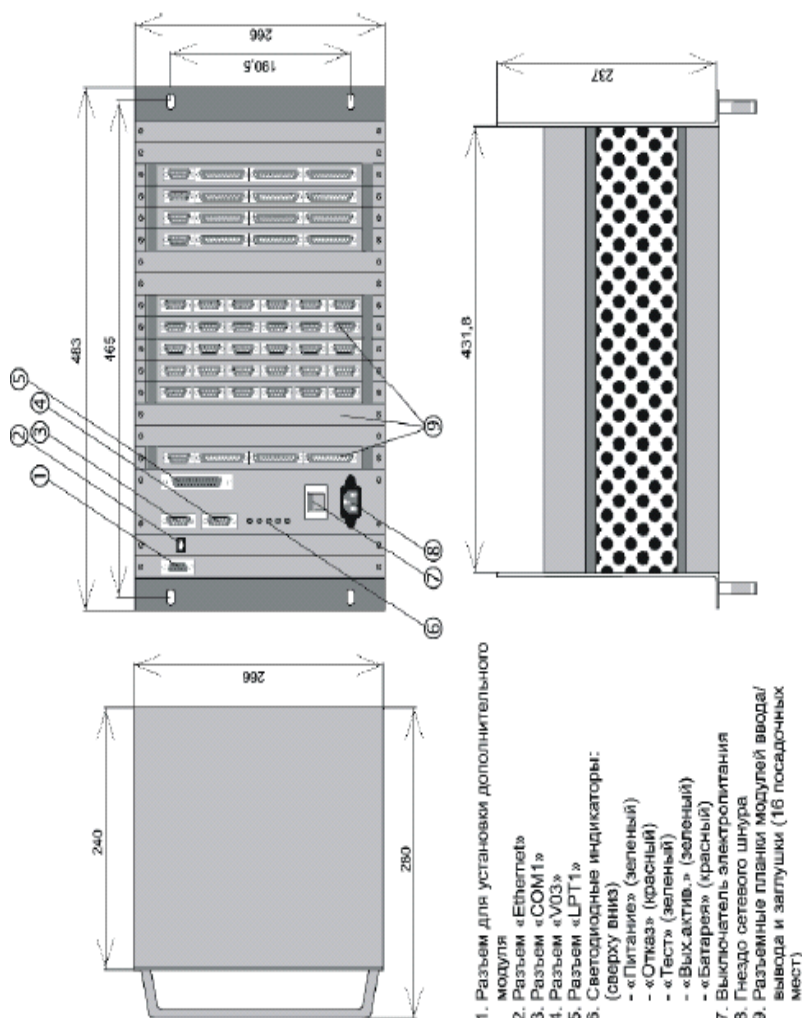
Габаритно-присоединительные размеры контроллера МФК, построенного на базе процессорного модуля microPC 5066
